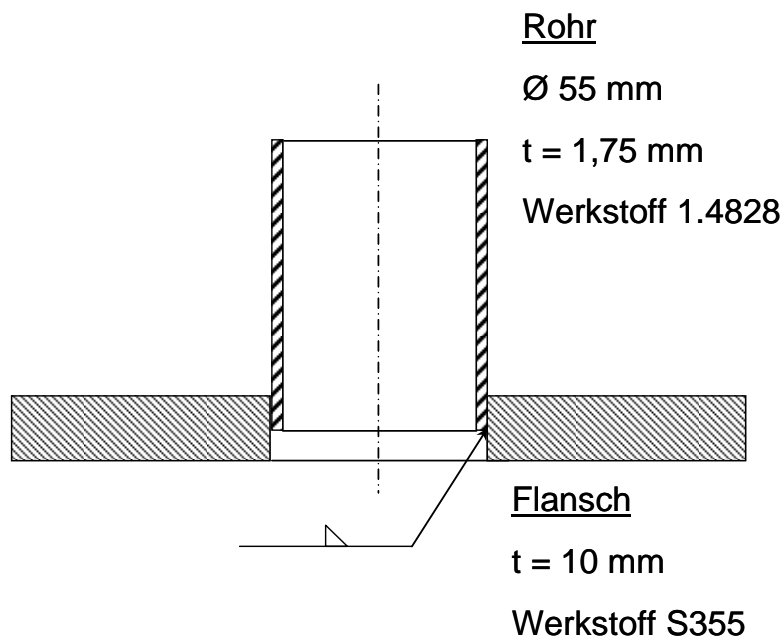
Aufbau Schweißversuch Blech-Rohr-Verbindung
